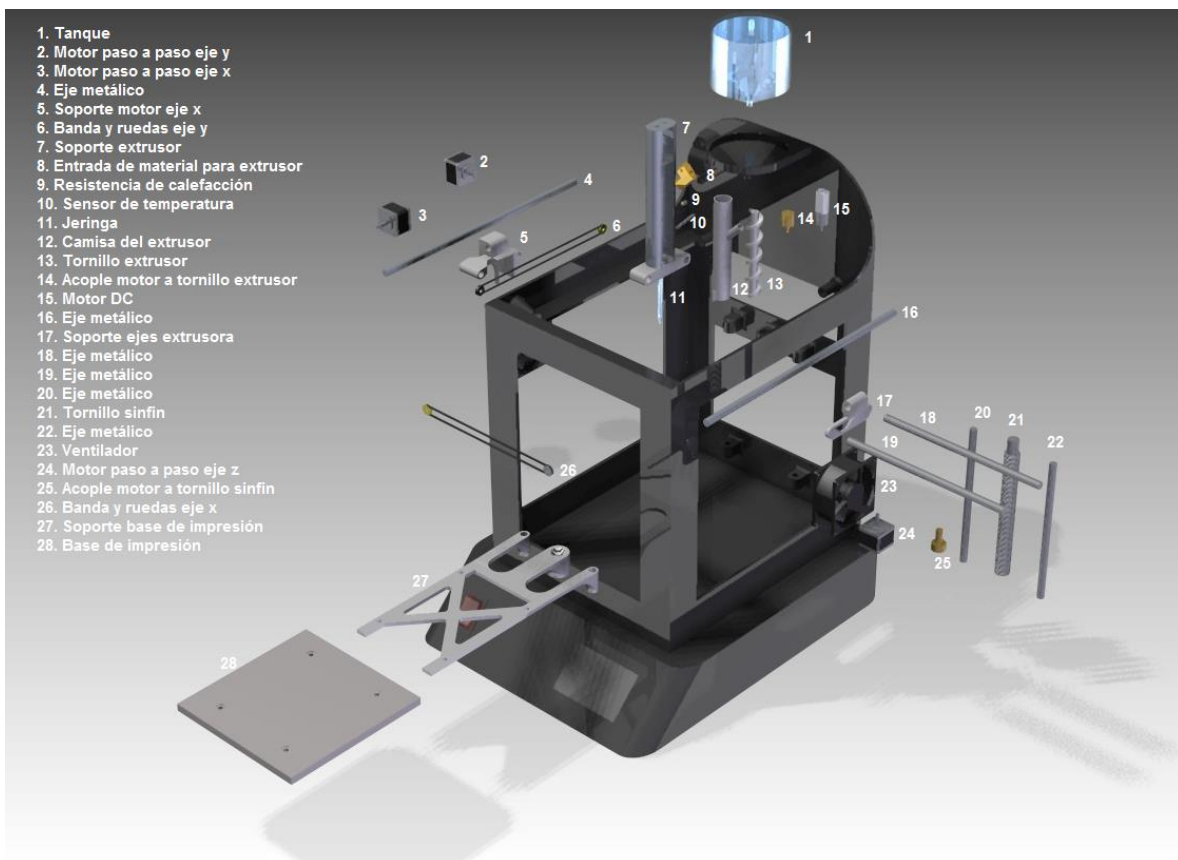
Explosionado de la impresora identificando cada una de sus partes
